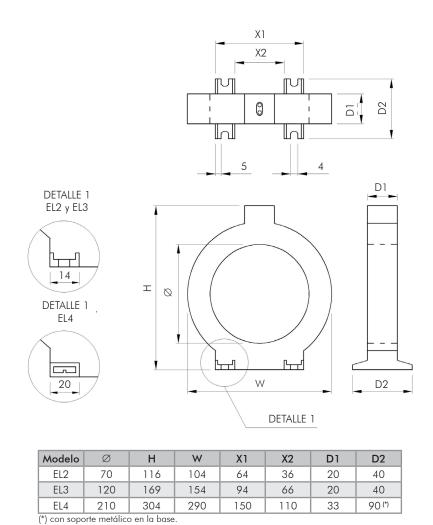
Dimensiones Sensores de Fuga a tierra EL2, EL3 y EL4 (mm)
